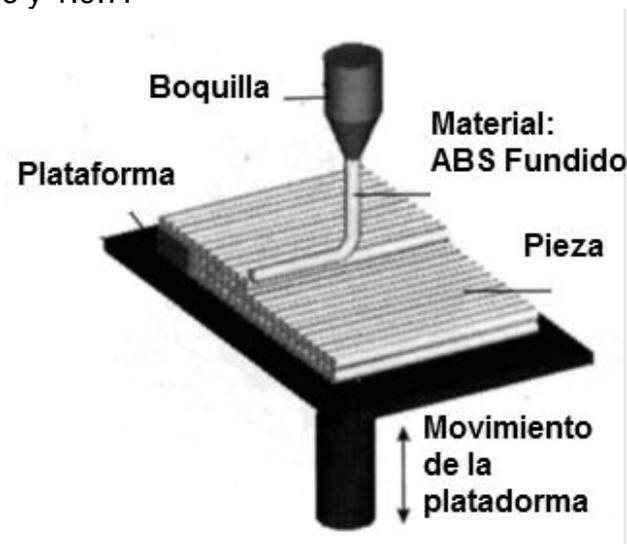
Sistema de impresión por Deposición Fundida
